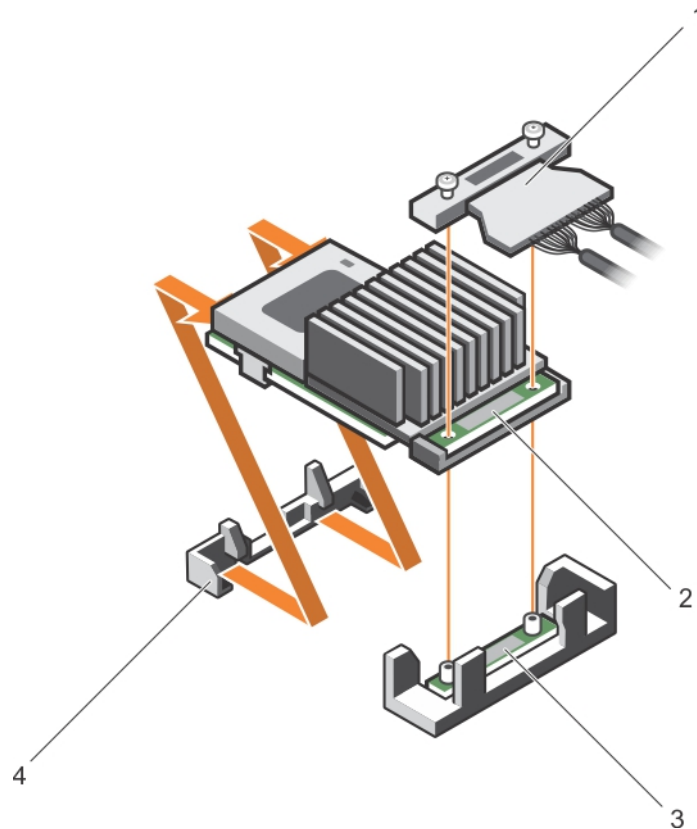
Rimozione e installazione della scheda del controller di storage integrato
